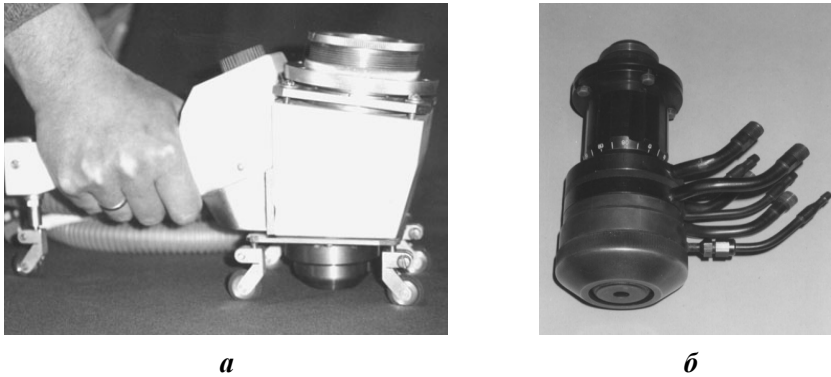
Інтегровані плазмотрон для гібридного лазерно-мікроплазмового зварювання з випромінюванням діодного лазера (*a*) і лазерно-дуговий плазмотрон з трубчастим термокатодом для лазерно-плазмового порошкового наплавлення з використанням  $\text{CO}_2$ -лазера (*б*)
